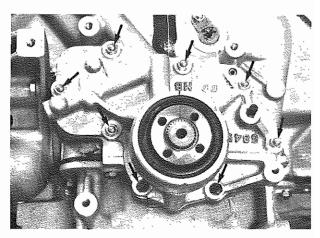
Dadi e viti di fissaggio Nuts and fixing screws
